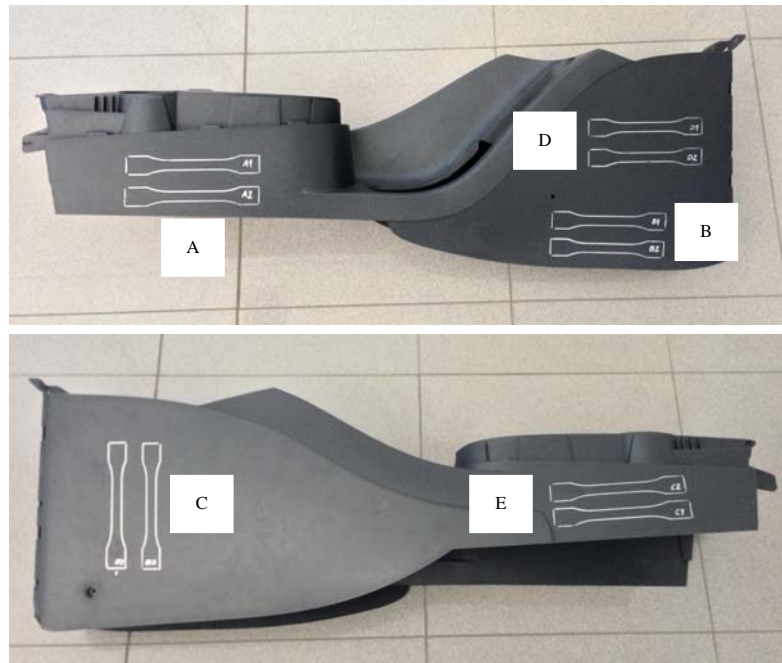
Áreas de extracción de planchas para ensayo, pieza Cuerpo Consola central
